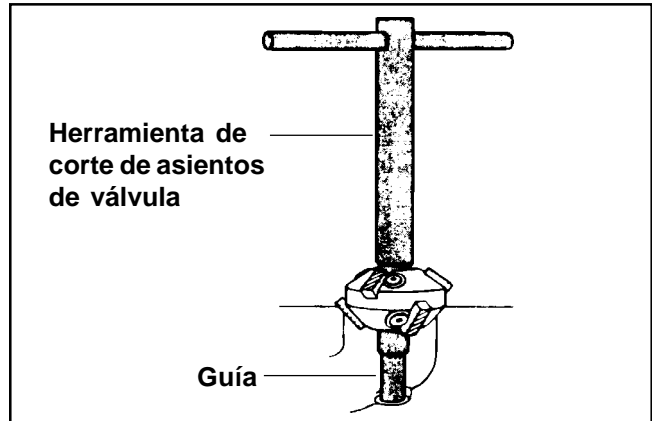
Herramienta de corte de asientos de válvula típica.
